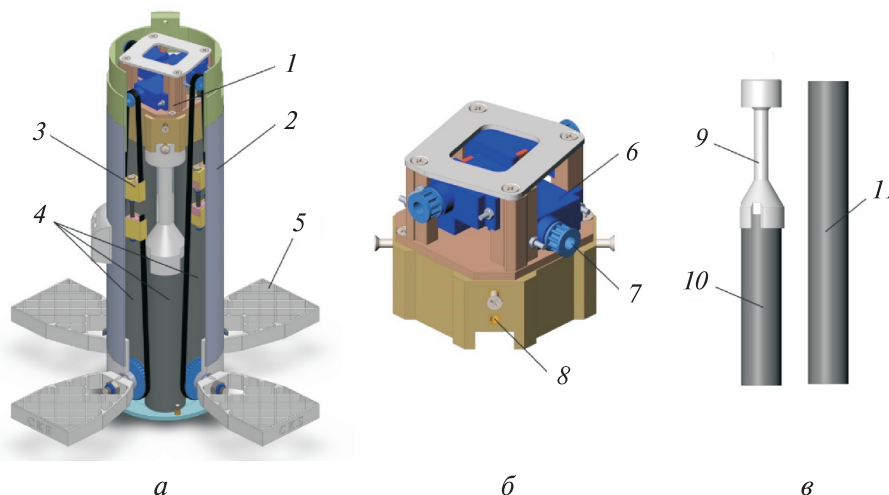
Общий вид двигательного отсека (а), блока сервоприводов (б) и двигательной установки (в):
